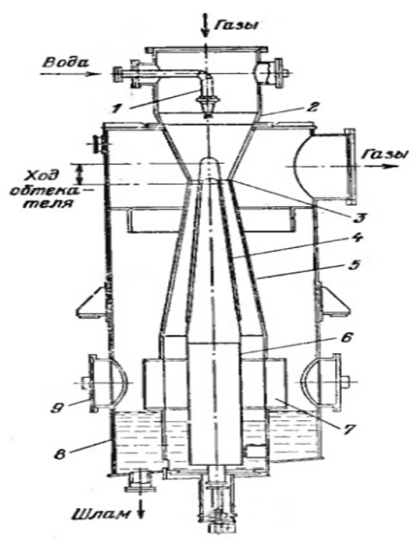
Скруббер Вентури с регулируемым сечением кольцевой горловины: 1 – форсунка; 2 – конфузор; 3 – горловина; 4 – регулирующий конус; 5 – диффузор; 6 – направляющий шток; 7 – центробежный завихритель; 8 – корпус каплеуловителя; 9 – люк⁶
